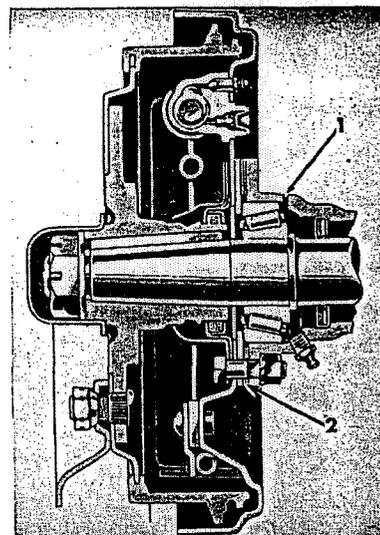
MOYEU ET ROULEMENT DE ROUE ARRIERE
